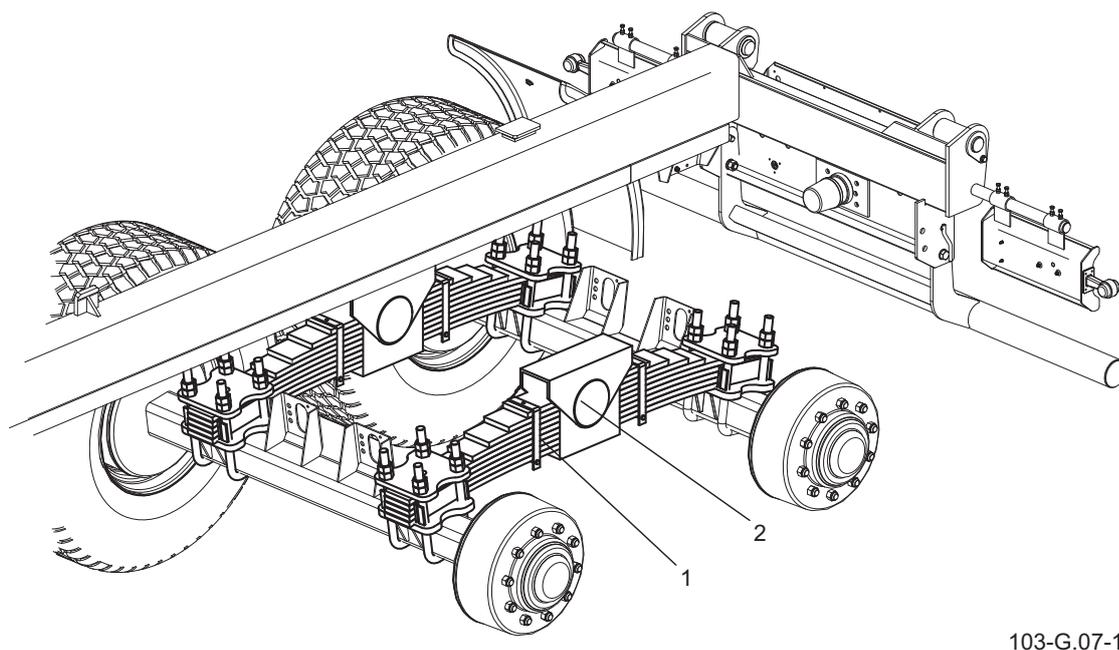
Рессорная подвеска типа "бу́ги"
